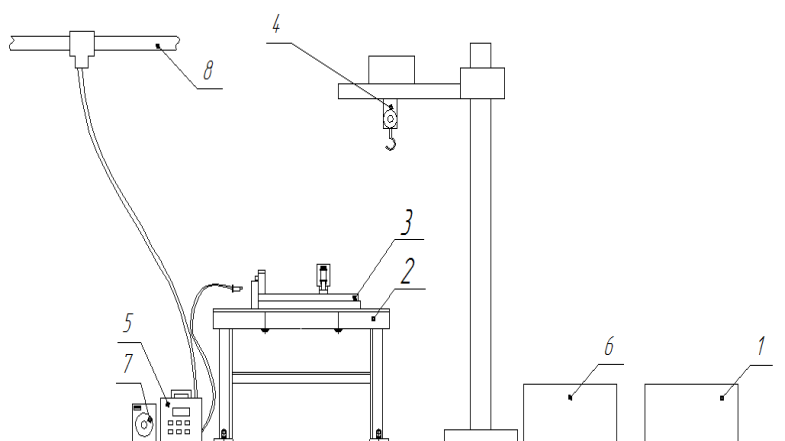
Схема компоновки рабочего места сварки узла №2:
